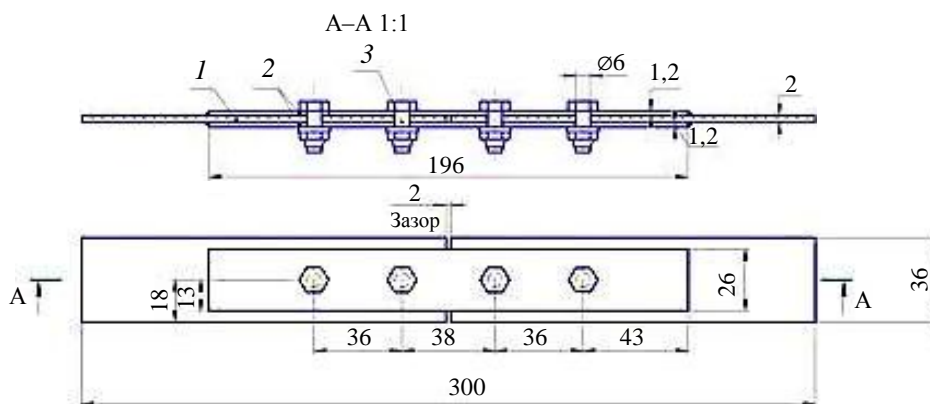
Эскиз конструктивно-подобного образца с применением четырехболтового соединения для испытаний системы противокоррозионной защиты: 1 – алюминиевый сплав; 2 – углепластик; 3 – крепеж
